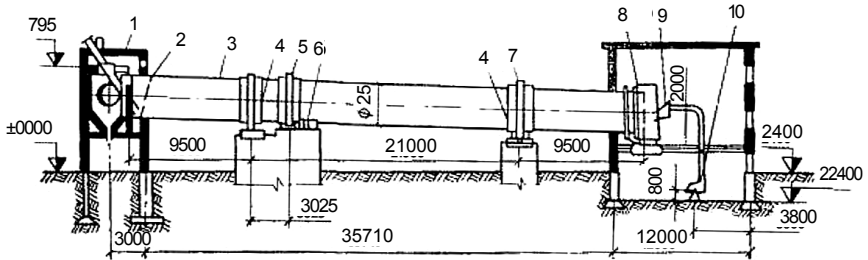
Схема обертової печі для випалювання керамзиту довжиною 40 м і діаметром 2,5 м: 1 — пилоосаджувальна камера; 2 — завантажувальна воронка; 3 — корпус печі; 4 — роликоопори; 5 — зубчаста шестерня; 6 — привод печі; 7 — бандаж; 8 — головка печі; 9 — пальник (форсунка); 10 — дуттєвий вентилятор
